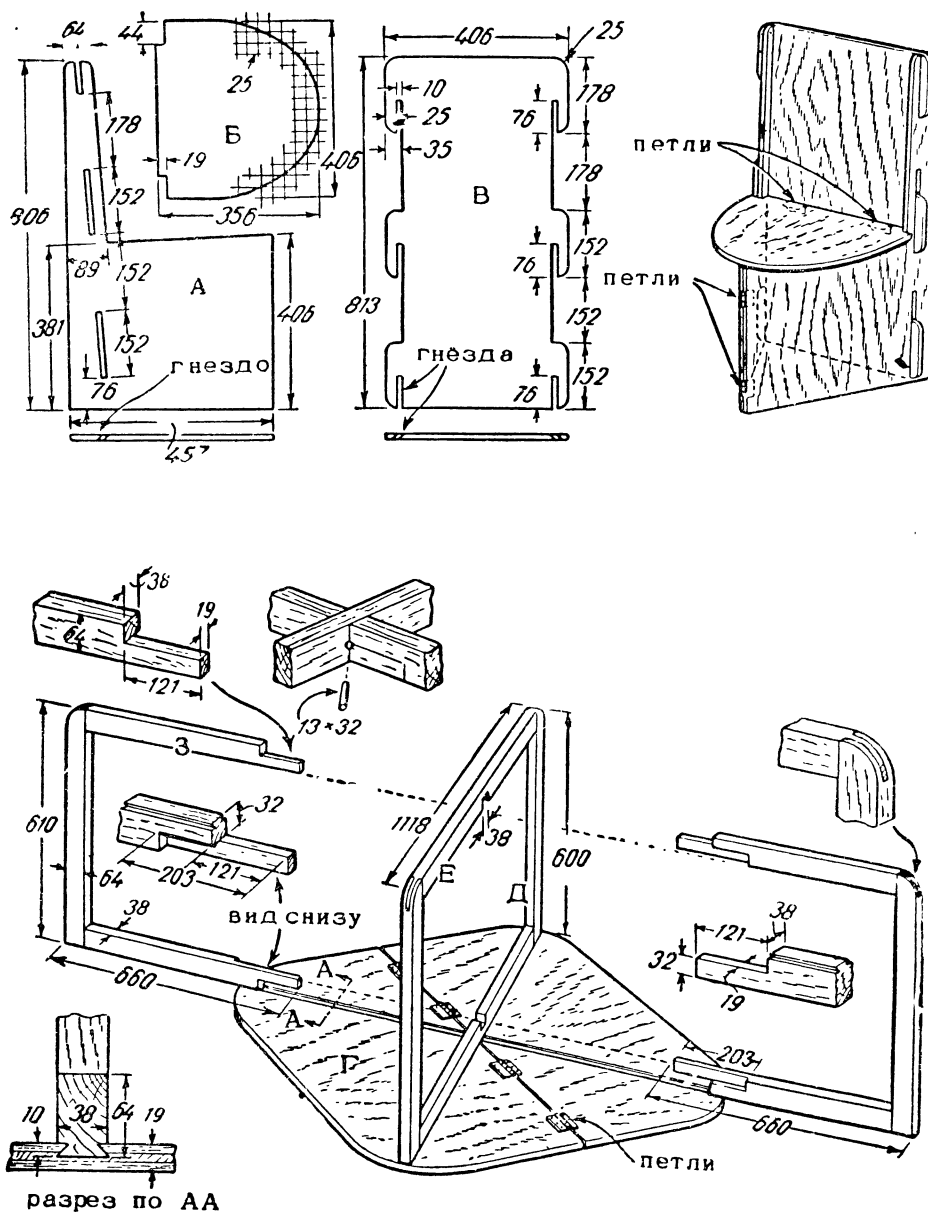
Детали сборки стула, шаблон для изготовления сидения (размер клеток — 25 мм) и детали сборки стола.
